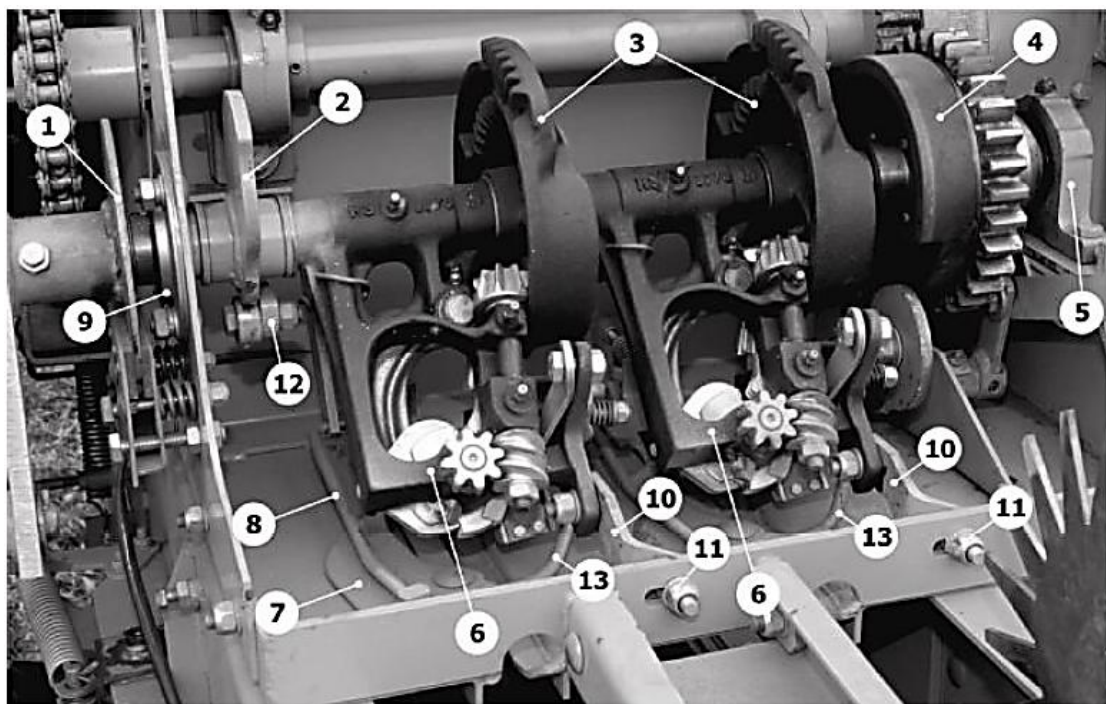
Обвязывающий механизм: 1 – тормоз обвязывающего механизма; 2 – кулачок; 3 – диск ведущий; 4 – муфта включения обвязывающего механизма; 5 – подшипниковая опора; 6 – вязальный аппарат; 7 –рычаг, направляющий шпагат; 8 – тяга; 9 – подшипниковая опора; 10 – кронштейн; 11 – болт; 12 – ось с роликом; 13 – захват
